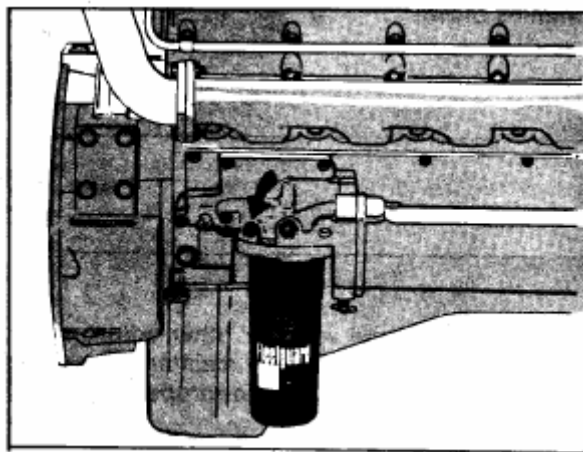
(OM1002L). Точка заливки системы смазки - двигатель VT-903 C.I.D
